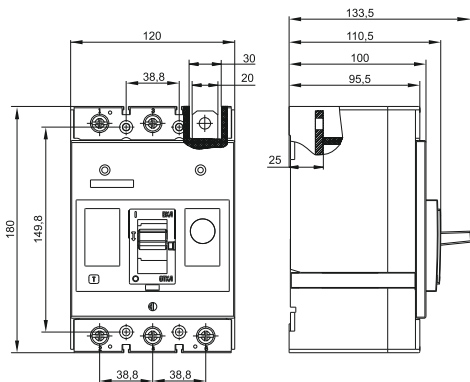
Габаритные и установочные размеры выключателя VA44-37 / Figure 7 — Overall and installation dimensions of the switch VA44-35 / 8-сурет — BA44-37 ажыратқышының габариттік және орнатқыш өлшемдері / Figura 8 — Dimensiunile generale și de montare ale întreruptorului VA44-37
